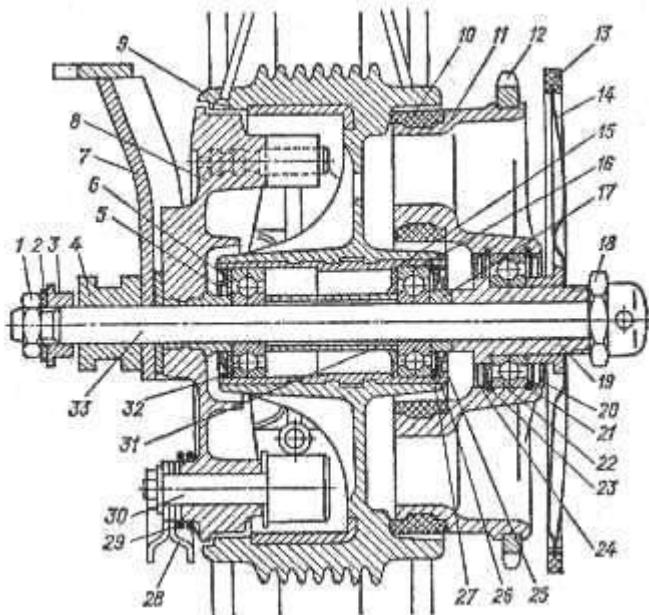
Поперечный разрез ступицы колеса и ведомой звездочки задней цепной передачи:
